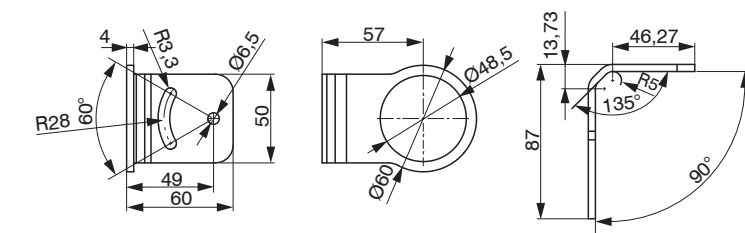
Maßzeichnung Montagewinkel, Abmessungen in mm, nicht maßstabsgetreu
